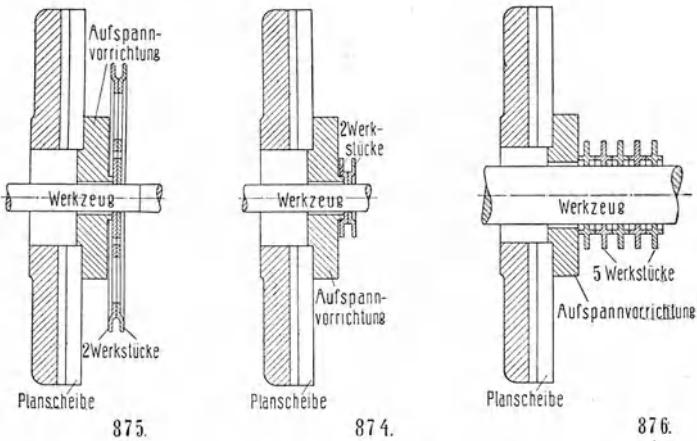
182. Schnitte durch Werkzeug und Werkstücke.
